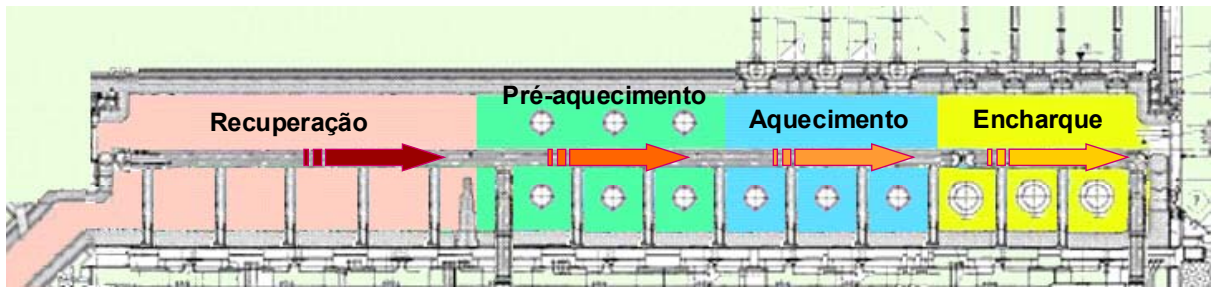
Corte longitudinal do Forno Walking Beam 2.
